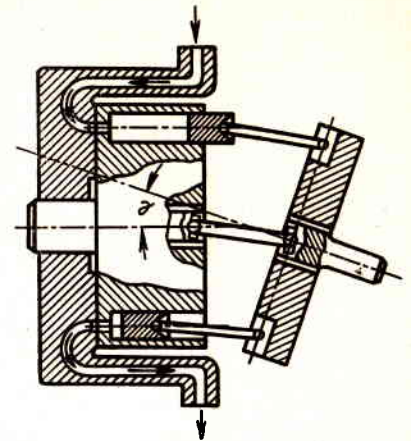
Esquema de una bomba rotatoria de émbolo con bloque inclinado
